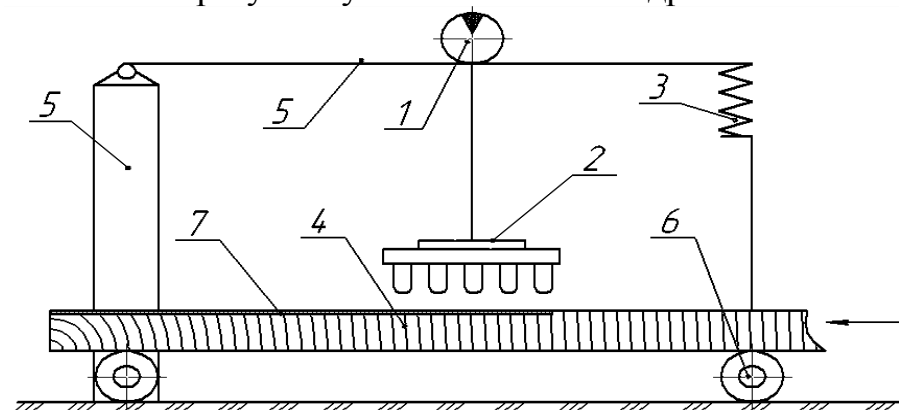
Установка для стационарной обработки поверхностей деревянных конструкций
